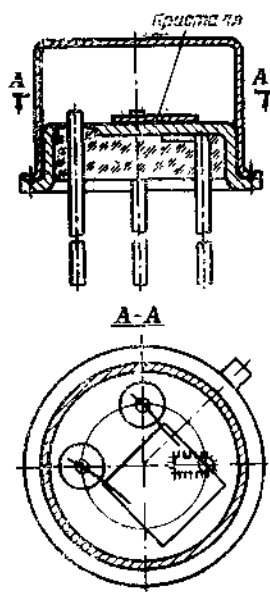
Конструкция корпуса КТ-22. Вариант для монтажа кристалла непосредственно на фланец корпуса.
